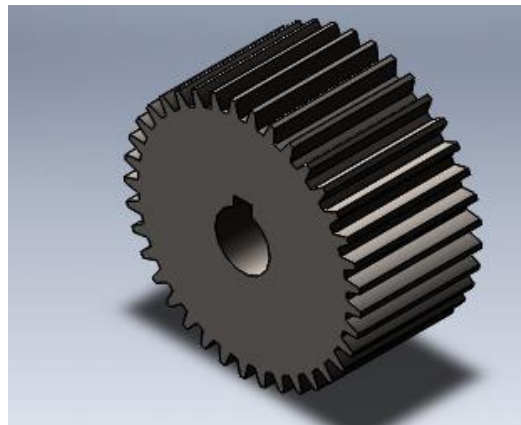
Engranaje resultante, Fuente: El Autor.
